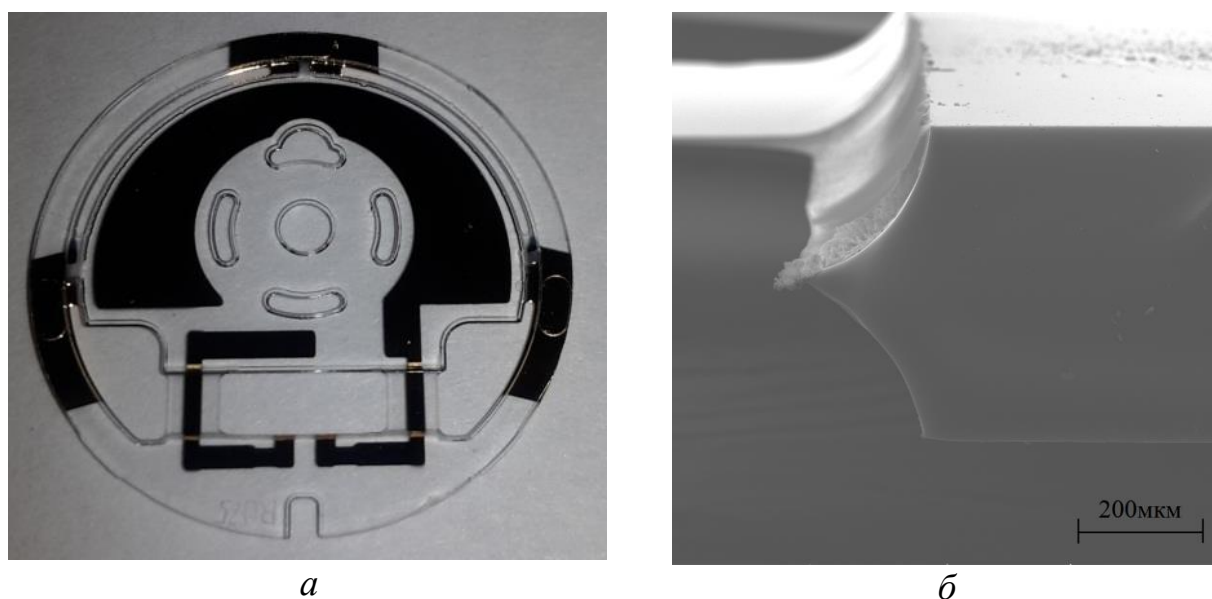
Внешний вид изготовленного чувствительного элемента с электродами (*а*) и форма его боковой поверхности (*б*)
